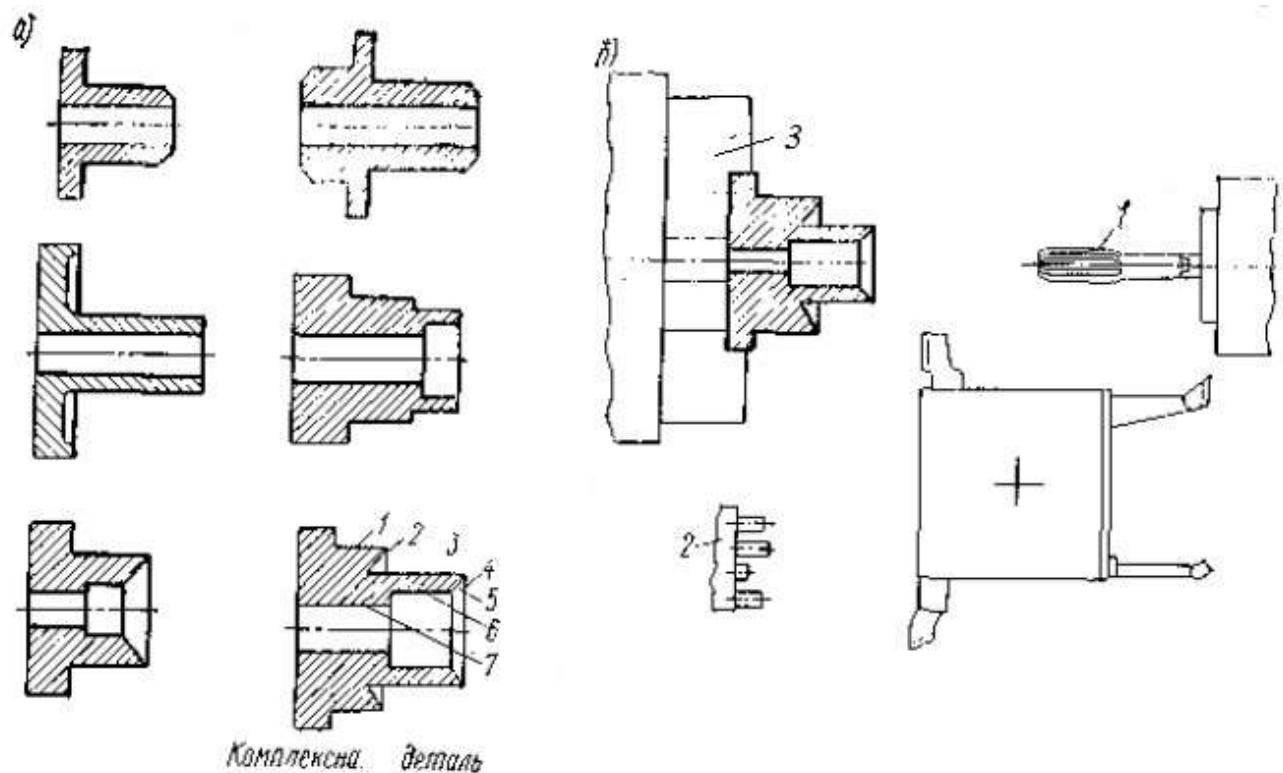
Використання комплексної деталі групи, оброблюваної на токарному верстаті.
